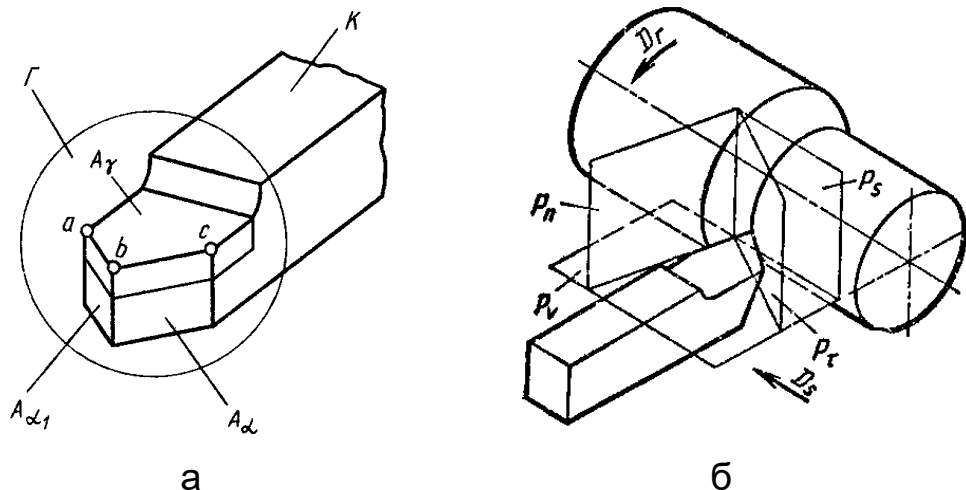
Элементы и координатные плоскости токарного резца
